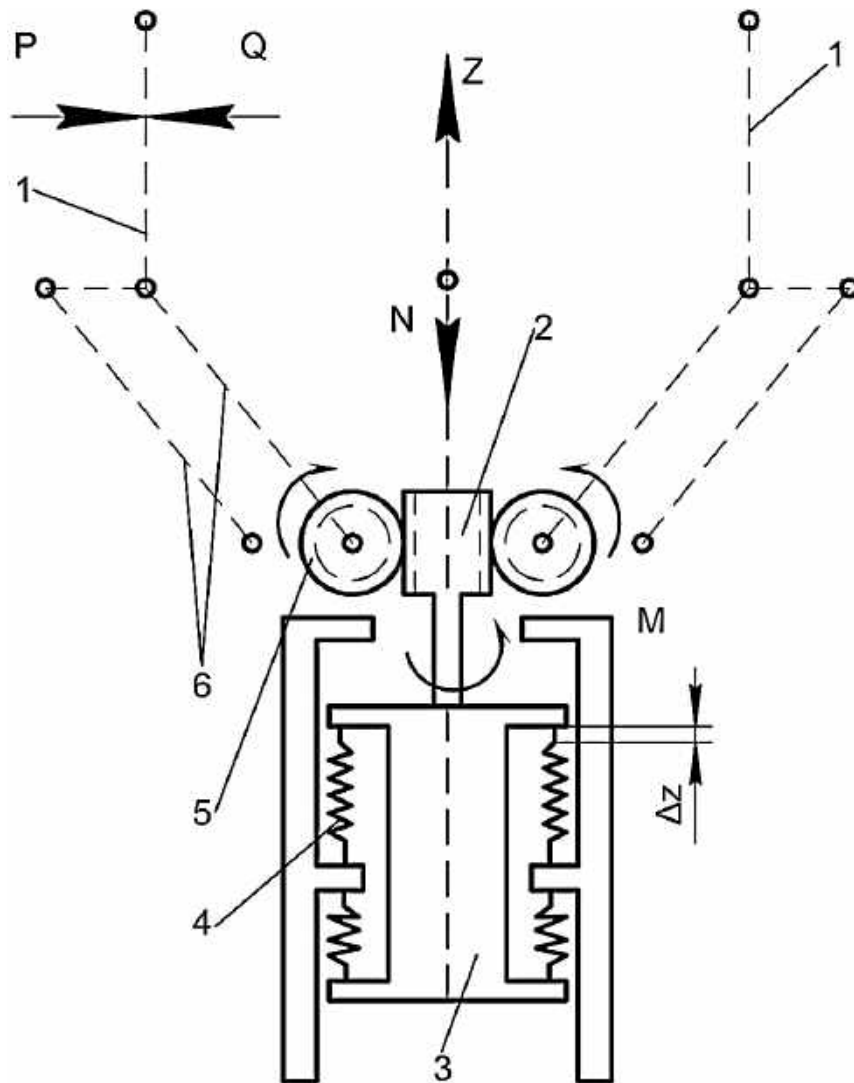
Кінематична схема вимірювання зусилля захоплення ЗП
